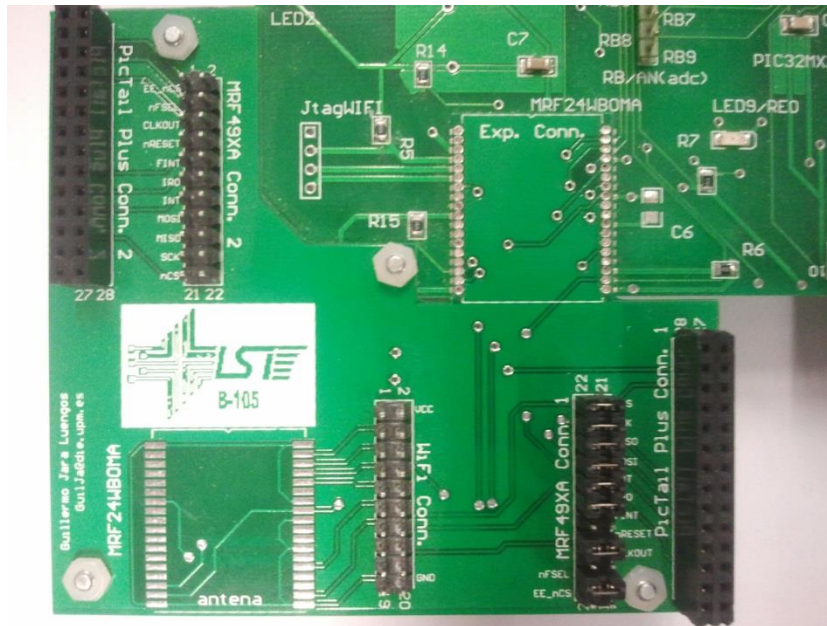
Placa de expansión soldada a la placa B105CNBOARD.
